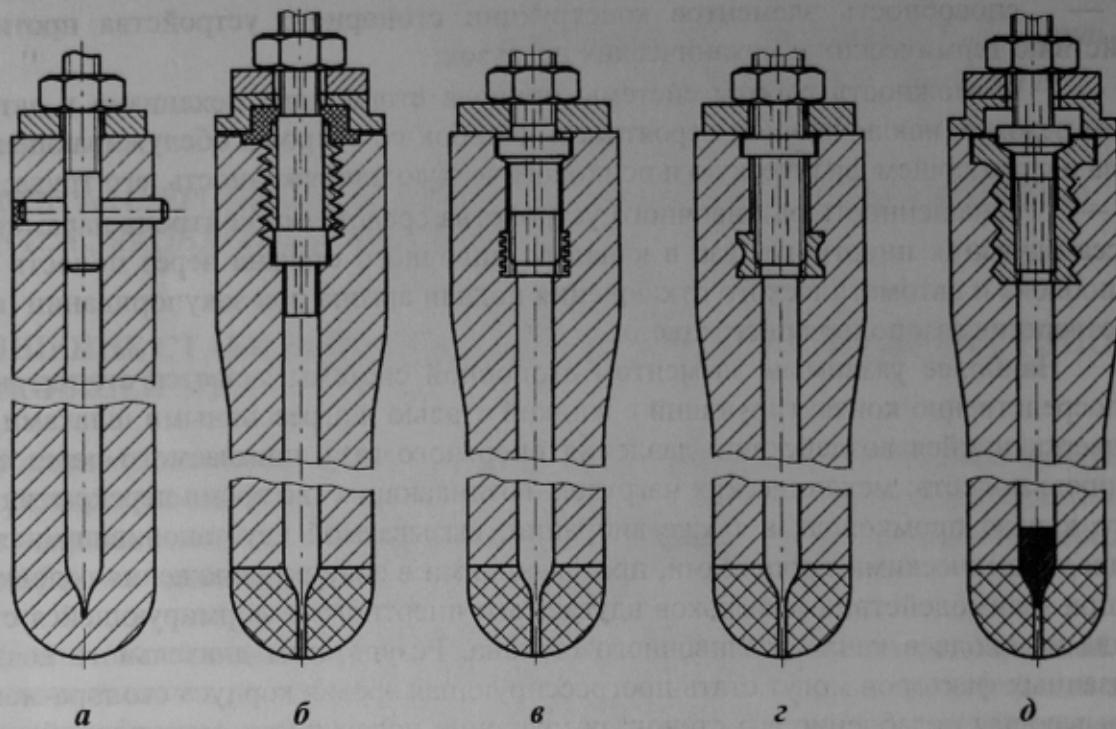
Схематическое представление способов крепления стопора-моноблока и штанги стопорного механизма: *а* — с помощью расклинивающей вставки; *б* — посредством керамической гайки, посаженной на раствор; *в* — посредством впрессованной металлической гайки; *г* — посредством впрессованной керамической гайки; *д* — посредством вкручиваемой металлической втулки с резьбой под гайку
